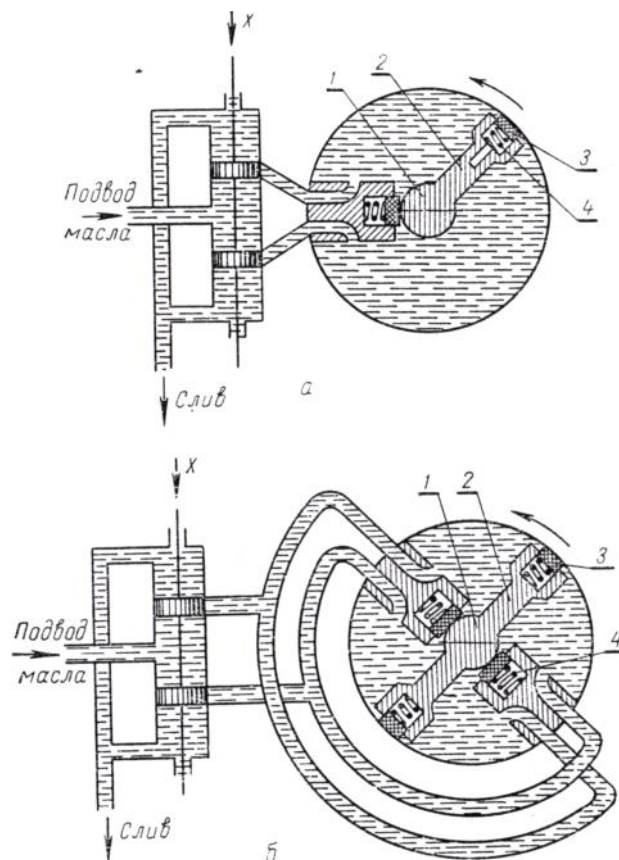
Гидравлический исполнительный механизм с вращающимся поршнем:
